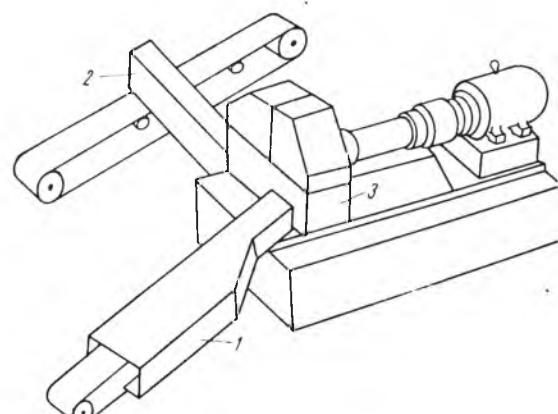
Схема рубительной машины со звукоизолирующими устройствами:
